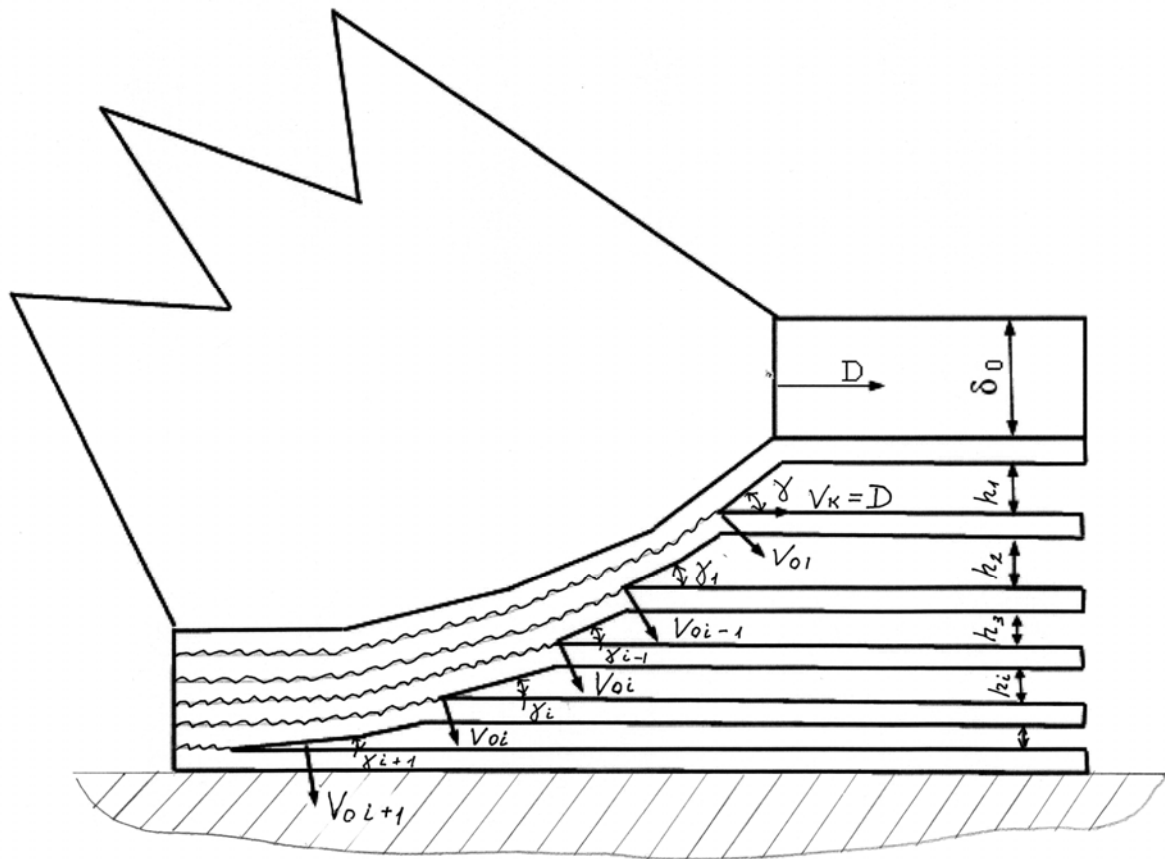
Схема соударения при пакетном способе сварки взрывом
